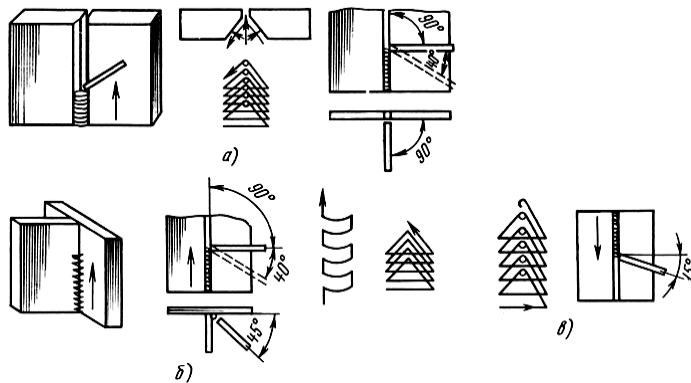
Положение и движения электрода при сварке в вертикальном положении:
